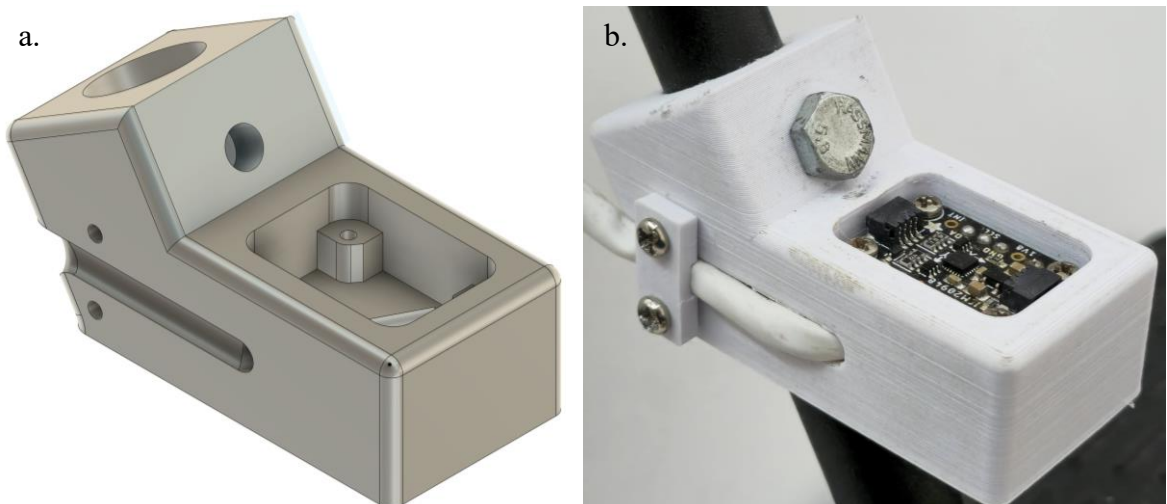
Modelagem em CAD dos S2 - Suporte do assento (seat pad), S3 - Suporte encosto (back pad).
